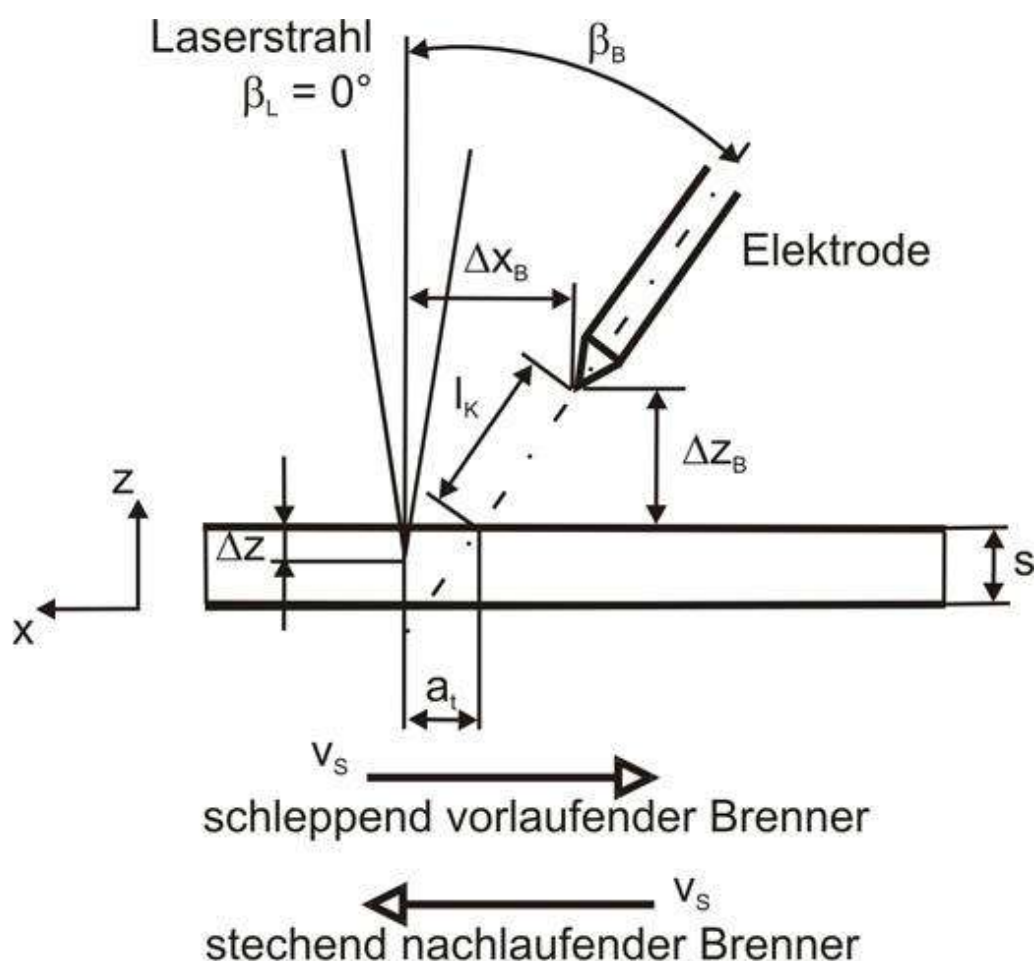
Технологічна схема лазерно-плазмового зварювання [83].
